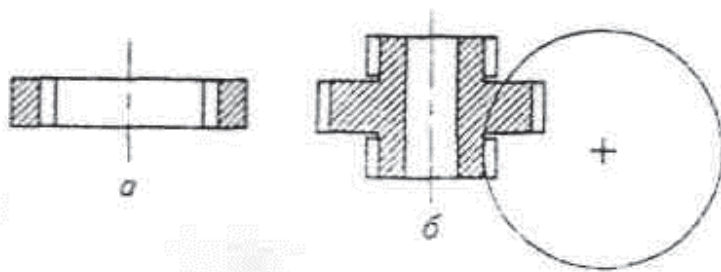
Некоторые разновидности зубчатых колес:
